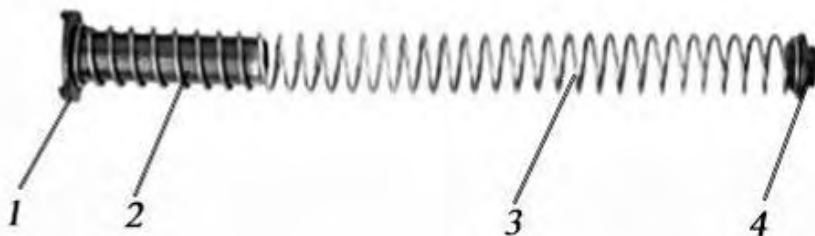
Возвратный механизм: 1 – головка; 2 – направляющий стержень; 3 – возвратная пружина; 4 – наконечник
